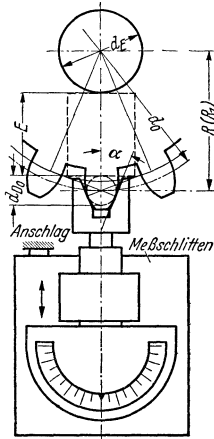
Zahndickenmessung mit Kimmmeßvorrichtung.
